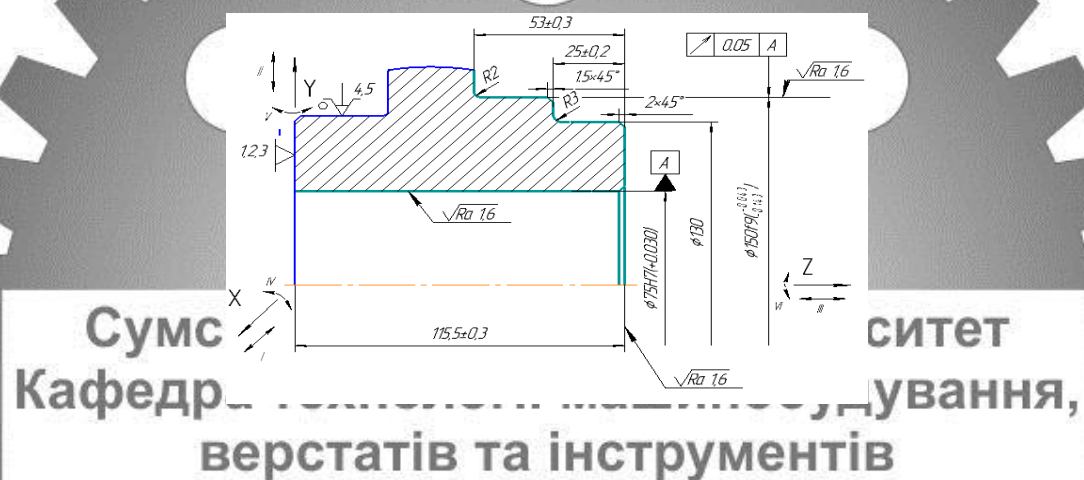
Схема базування заготовки втулки зубчастої на операції 040
